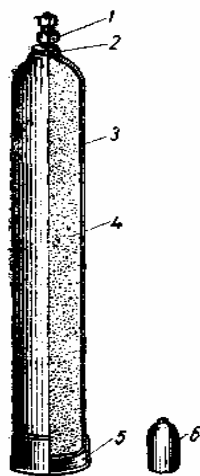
Балон для ацетилену в розрізі: 1 - вентиль; 2 - горловина; 3 — корпус; 4 - пориста маса; 5 — башмак; 6 — ковпак.
